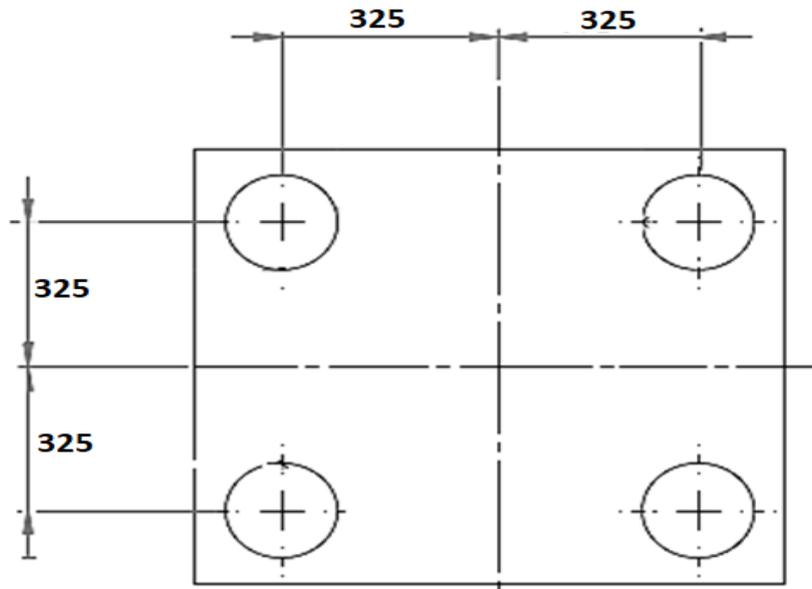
Schéma d'un plateau d'une presse 150T.
